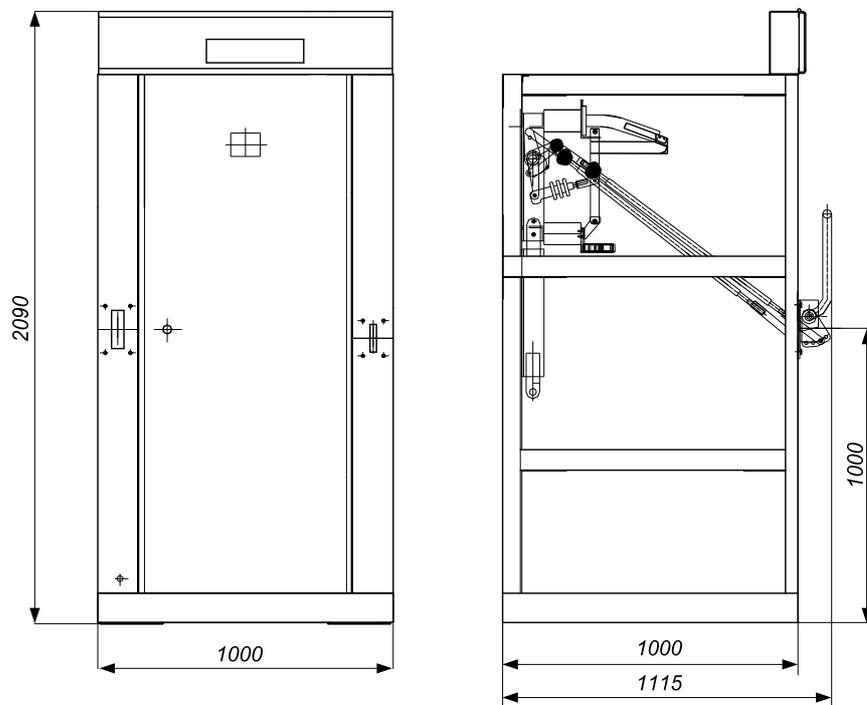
Внешний вид и габаритные размеры камер КСО-366К
